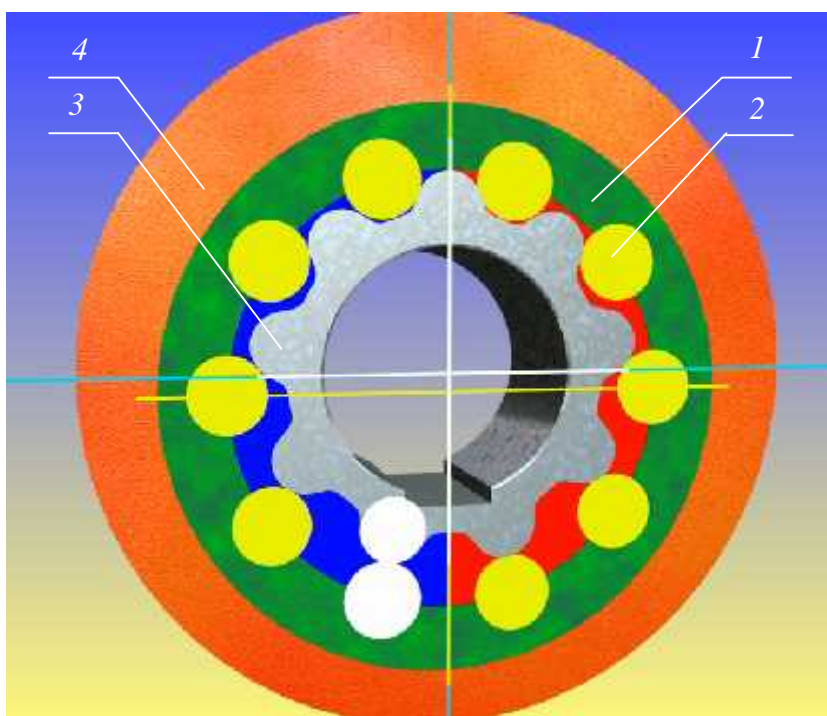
Компенсирование героторного движения вытеснителей с помощью смещения вытеснителей (роторов): 1 – охватывающий вытеснитель; 2 – ролики; 3 – охватываемый вытеснитель; 4 – корпус.
